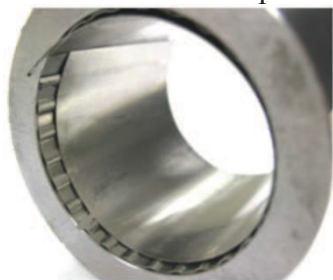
Лепестковые подшипники с подкладными упругими элементами
